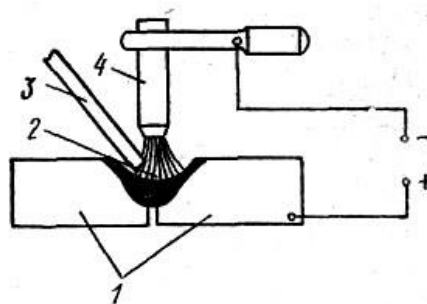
Ручне зварювання електродом, що не плавиться: 1 – основний метал; 2 – метал шва;
